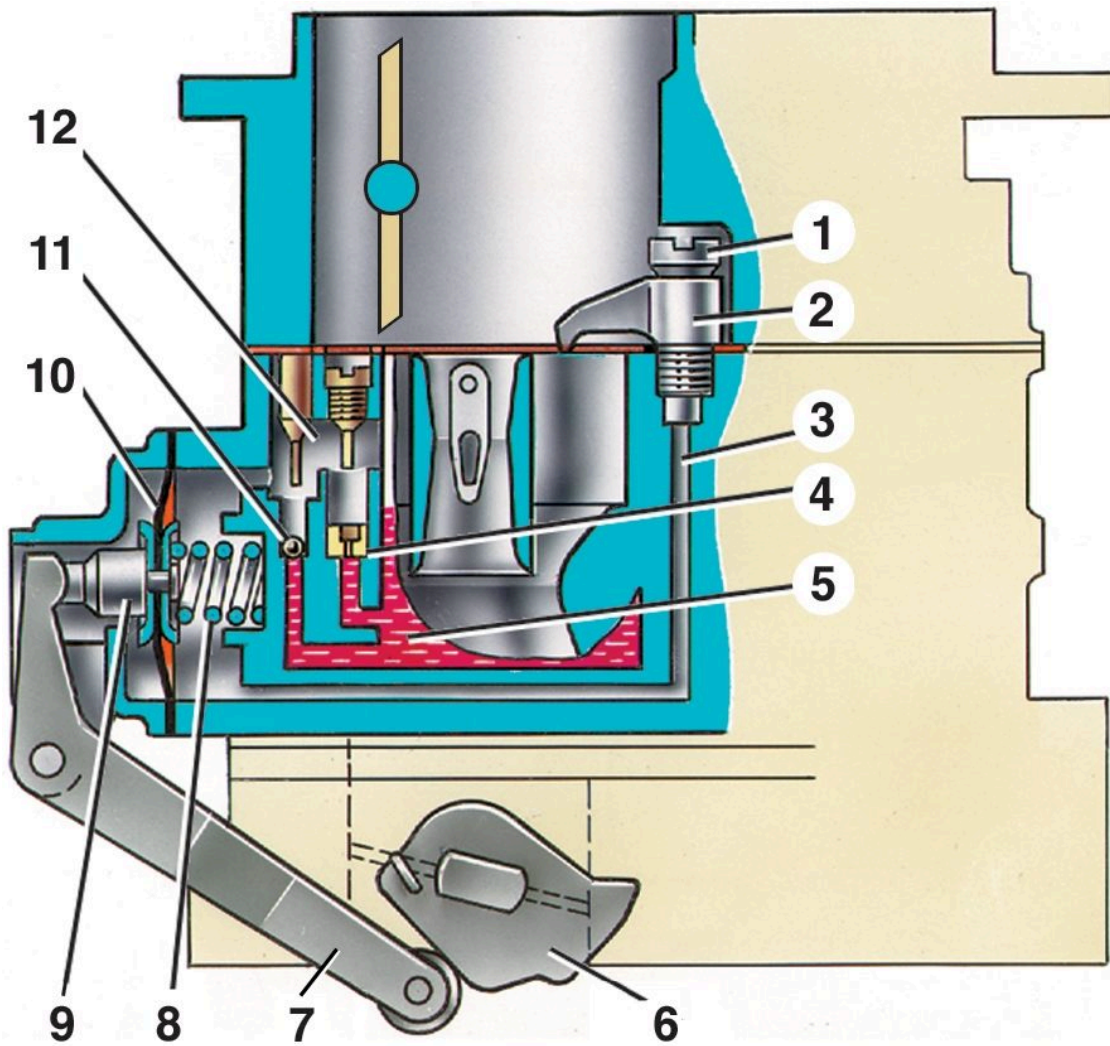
Схема прискорювального насоса карбюратора 2107-1107010: 1 - гвинт-клапан; 2 - розпилювач; 3 - паливний канал; 4 - пропускний жиклер; 5 - поплавкова камера; 6 - сектор привода прискорювального насоса; 7 - важіль привода; 8 - зворотна пружина; 9 - чашка діафрагми; 10 - діафрагма насоса; 11 - впускний кульковий клапан; 12 - камера парів насоса
